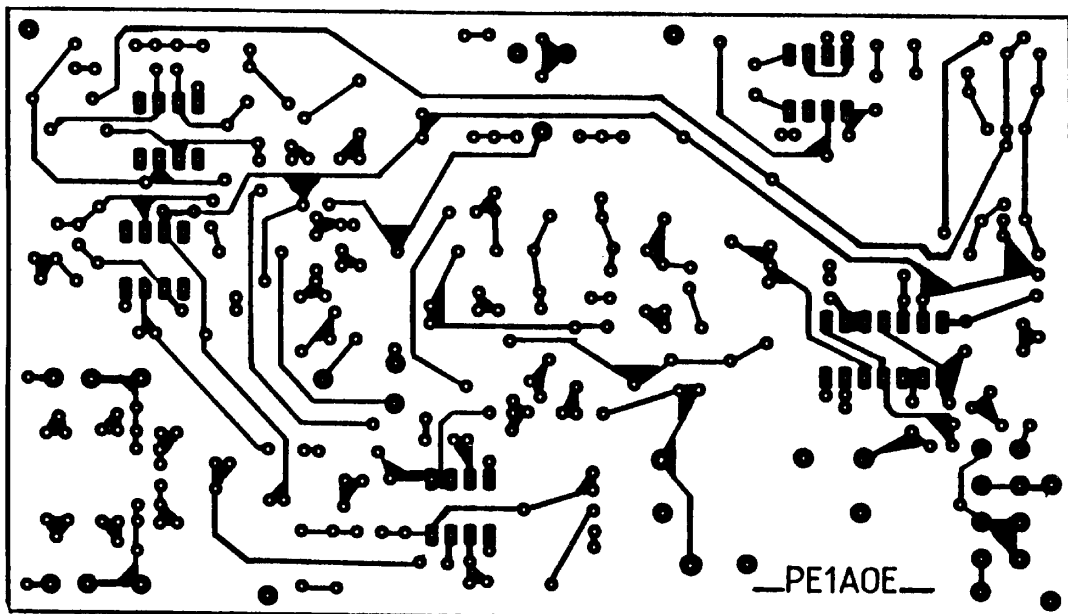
Printlay-out, de componentenzijde is geheel van koper.
